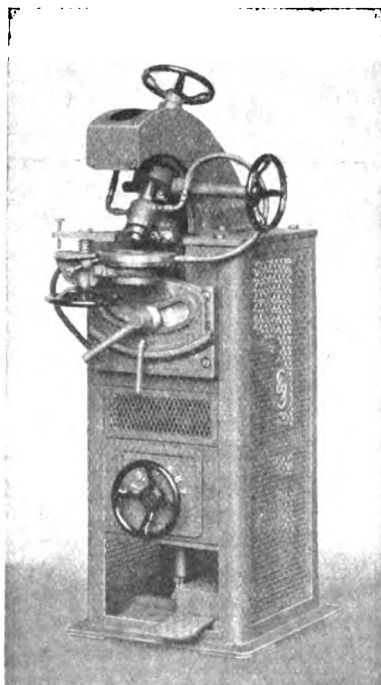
Edelstahl-Aufschweißmaschine.
